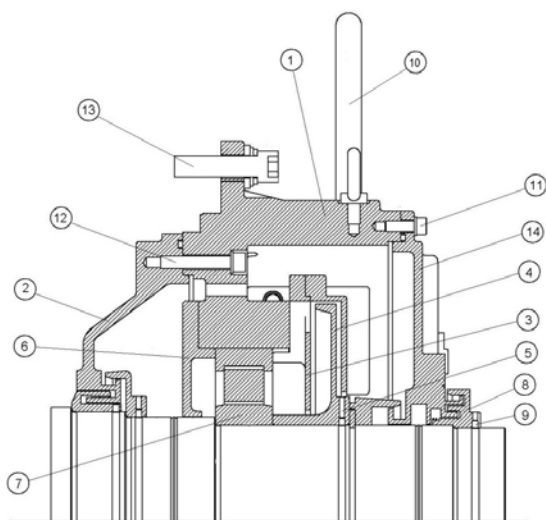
Детали подшипника качения с циркулирующей масла
